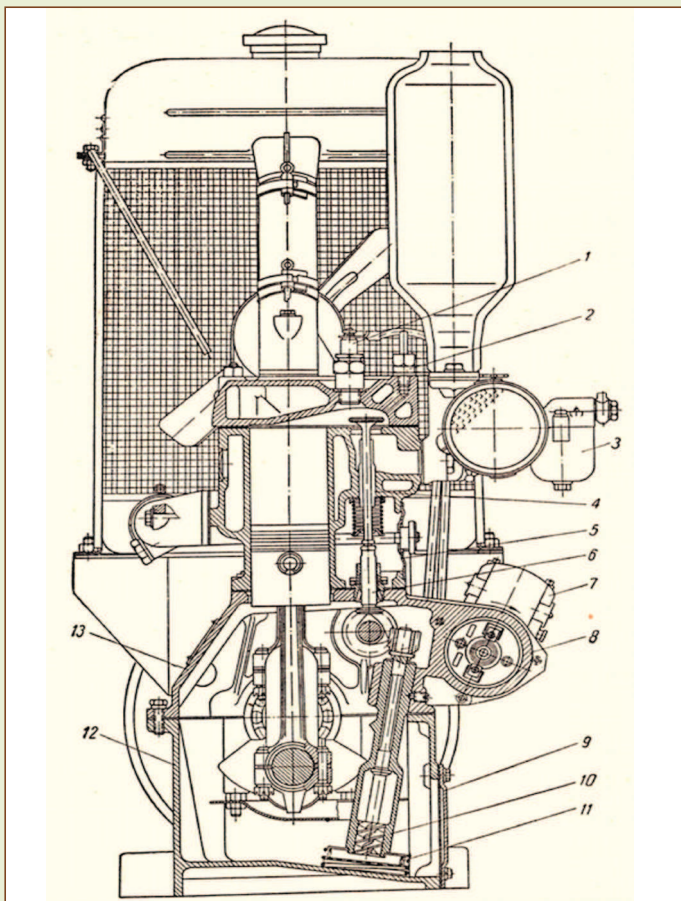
Поперечный разрез двигателя Л-6/3 [5. с.32]
